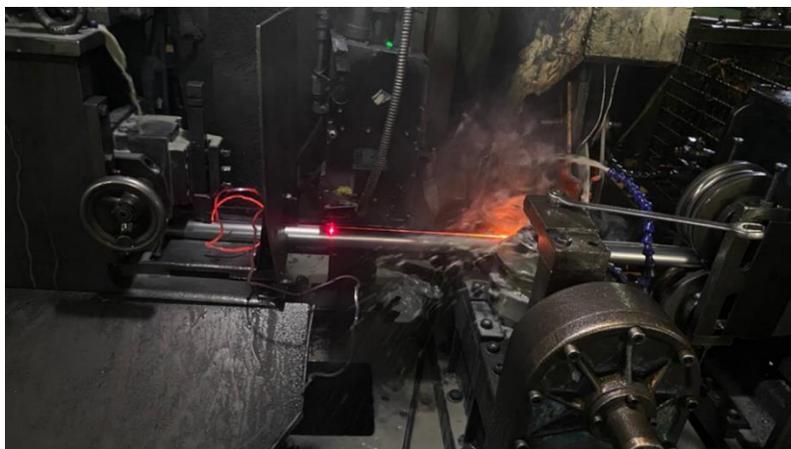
1 Fabricación de tubo mediante soldadura de inducción. Fuente CMA Automotive 2023
